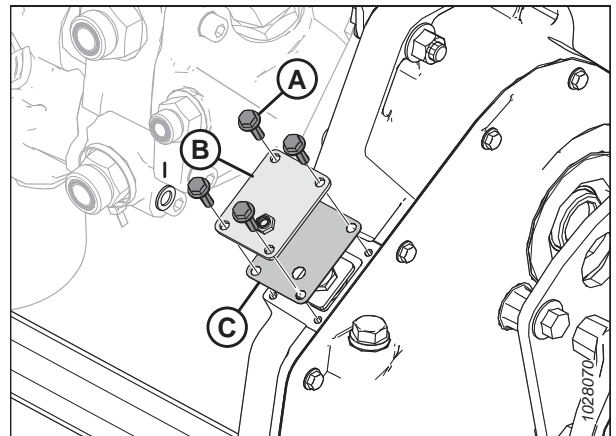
Hauptgetriebe mit Kettenspannerabdeckung
